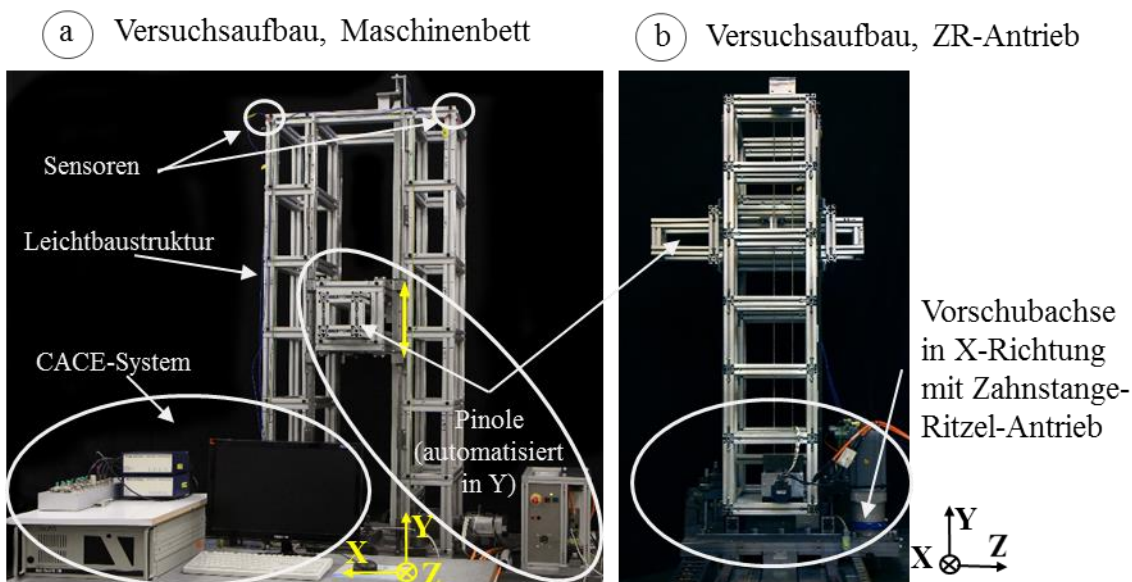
Laborprototyp einer Leichtbauwerkzeugmaschinenstruktur mit Fahrständerkinematik.
